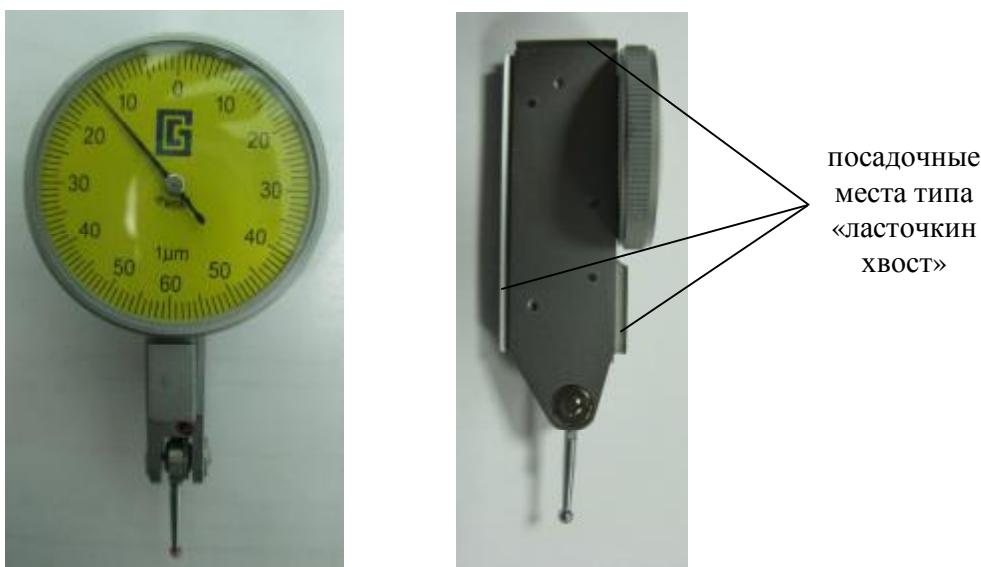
Общий вид индикаторов рычажно-зубчатых ИРБ тип I
